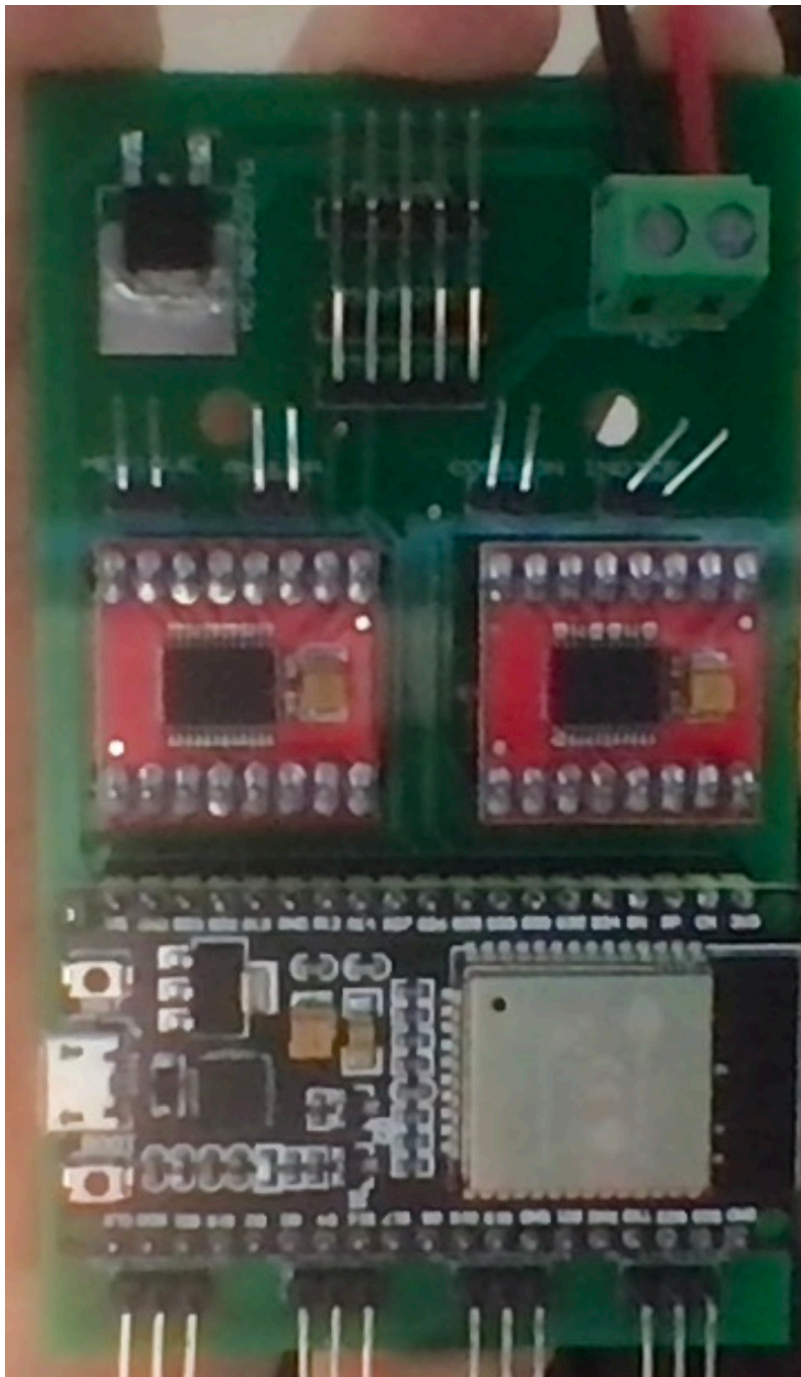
Primer diseño de PCB (ESP-WROOM32 WiFi™-Bluetooth™).
